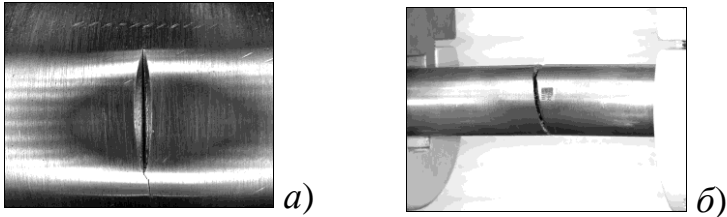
Загальний вигляд тріщини, що розвивається від концентратора напружень (а) та (б) фрагмента зруйнованої гнучкої труби
